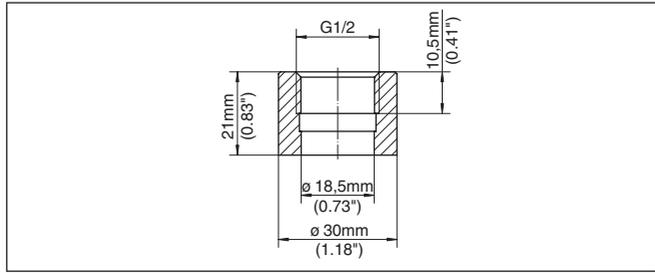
Dimensiones racor para soldar G $\frac{1}{2}$ (ISO 228-1) frontal rasante - VEGABAR 82
